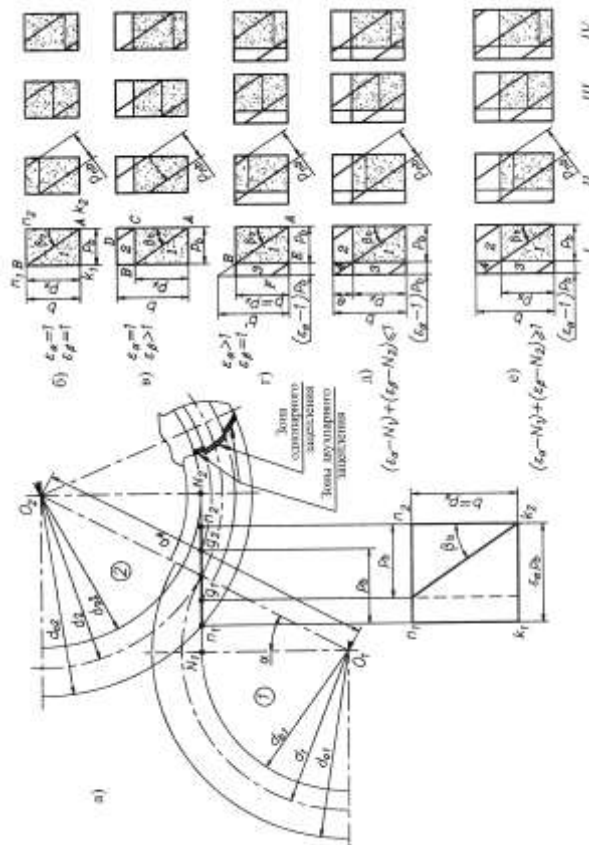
Положение линий контакта зубьев на поле зацепления для косозубых колес
